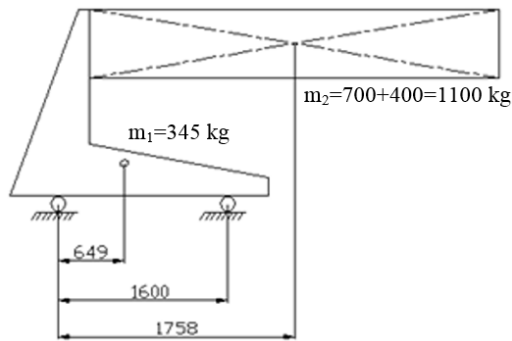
Draft rancangan welding fixture terpilih
